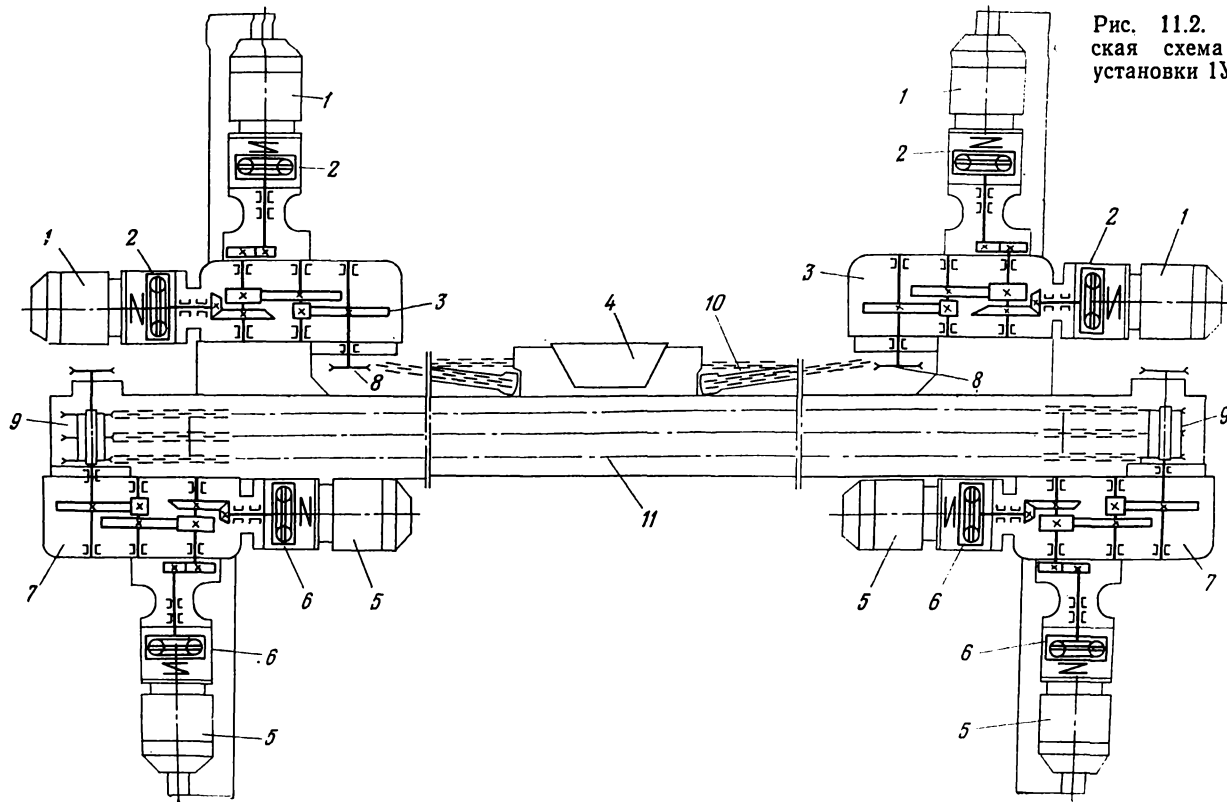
Кинематическая схема струговой установки 1УСБ67
